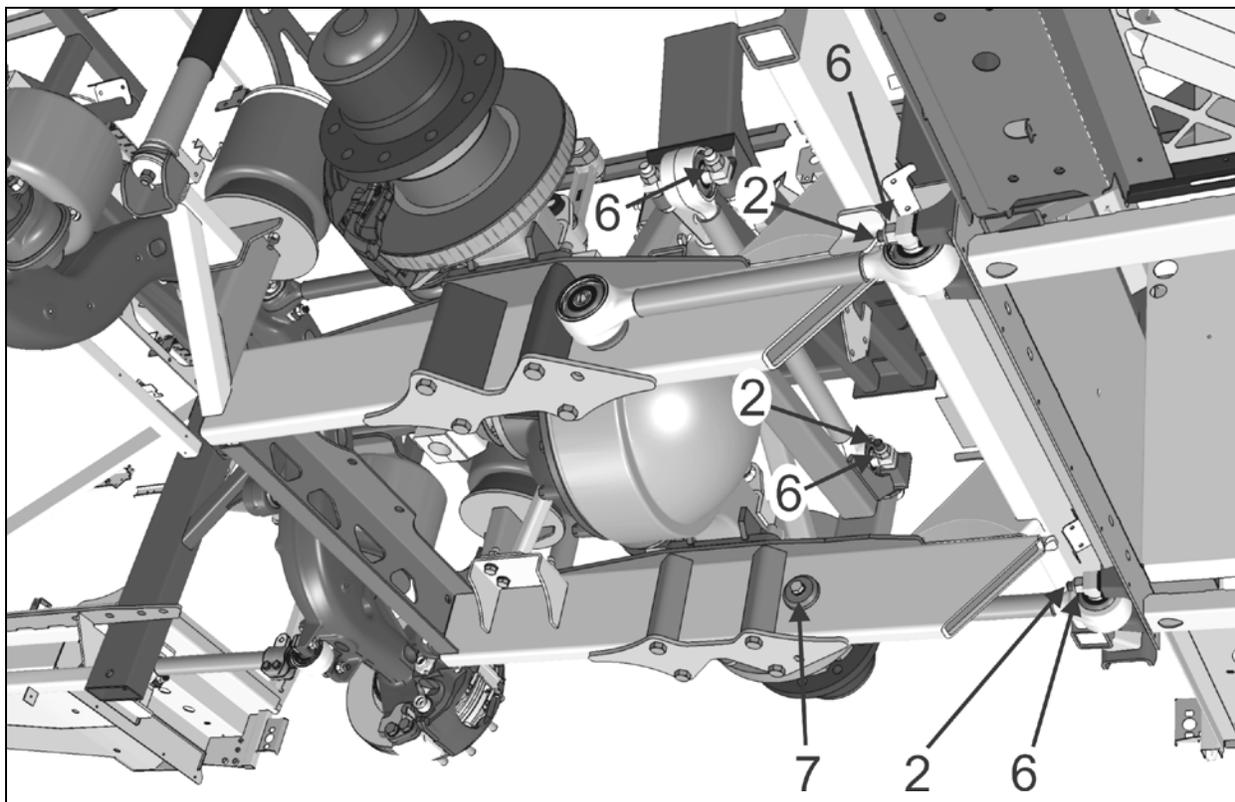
COUPLES DE SERRAGE – ESSIEU MOTEUR
